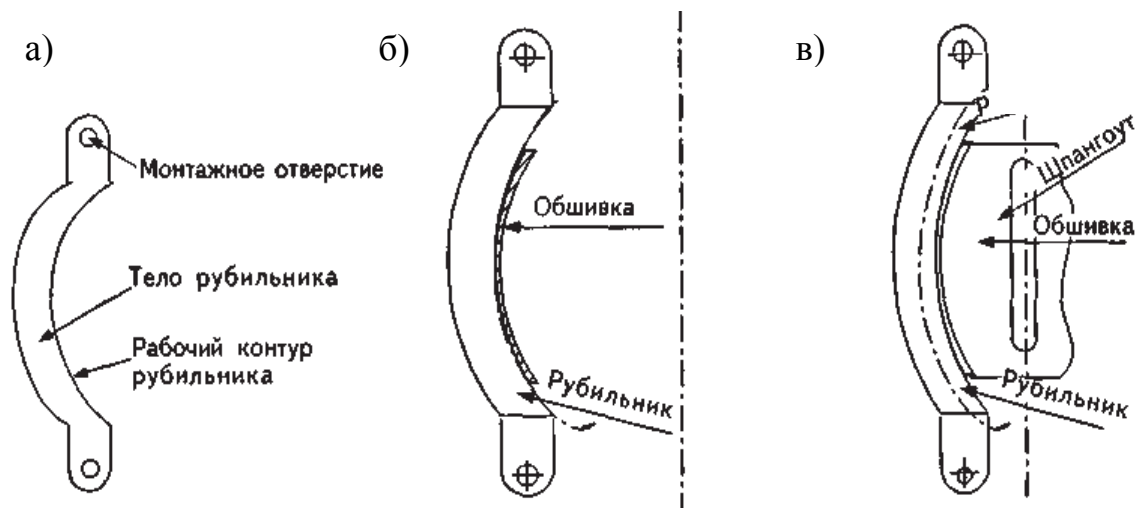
Типы рубильников: а – конструктивная схема рубильника; б – обшивочный (нормальный) рубильник; в – каркасный рубильник
